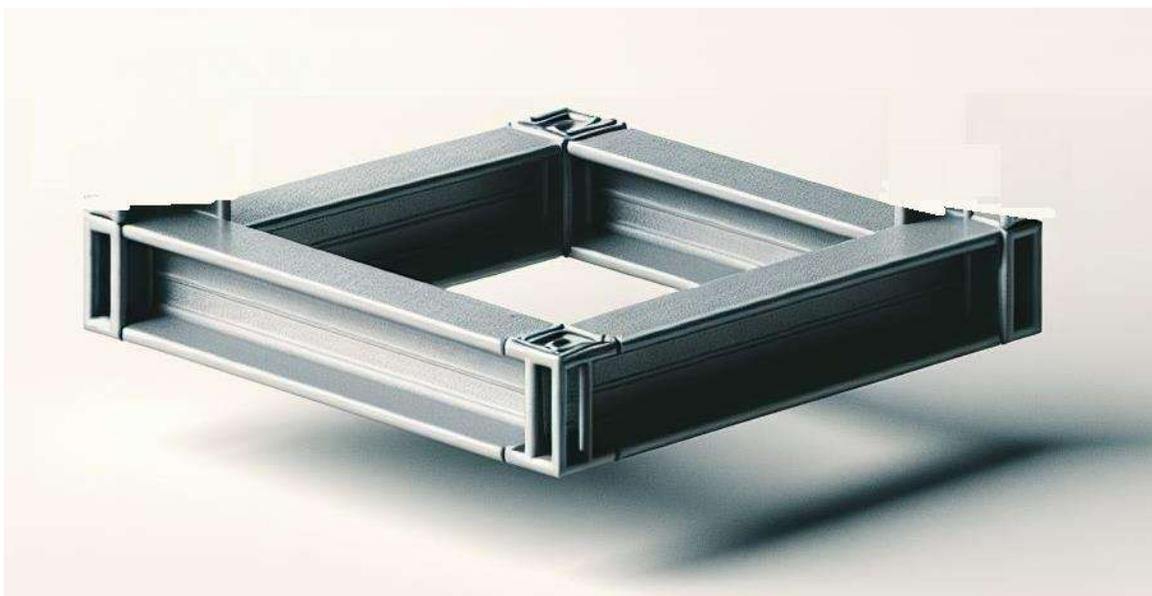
OpenAI. (2025). Fijación de barrenos y placas, imagen generada por IA.
